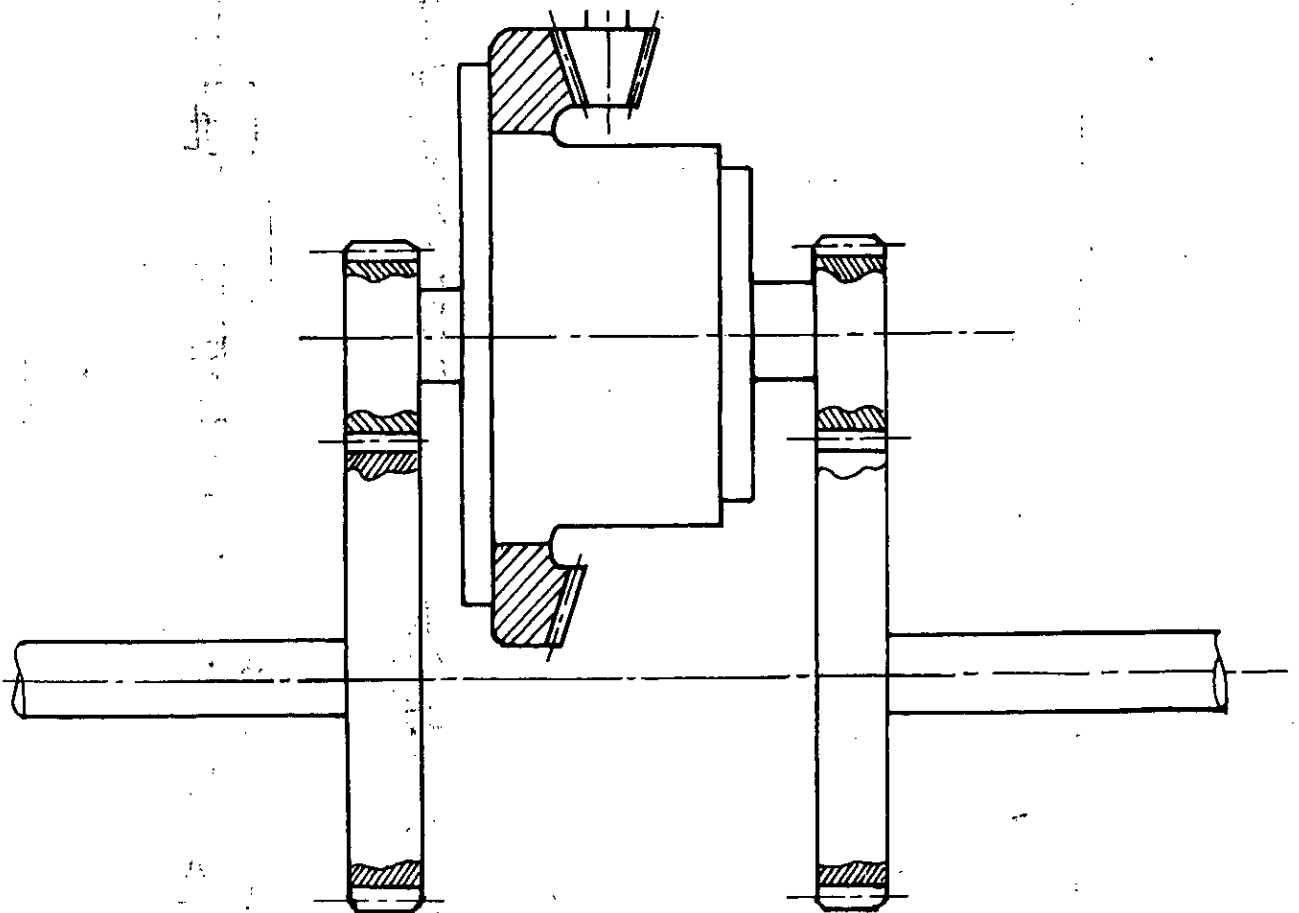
Ensemble des pièces inertielles du pont arrière
